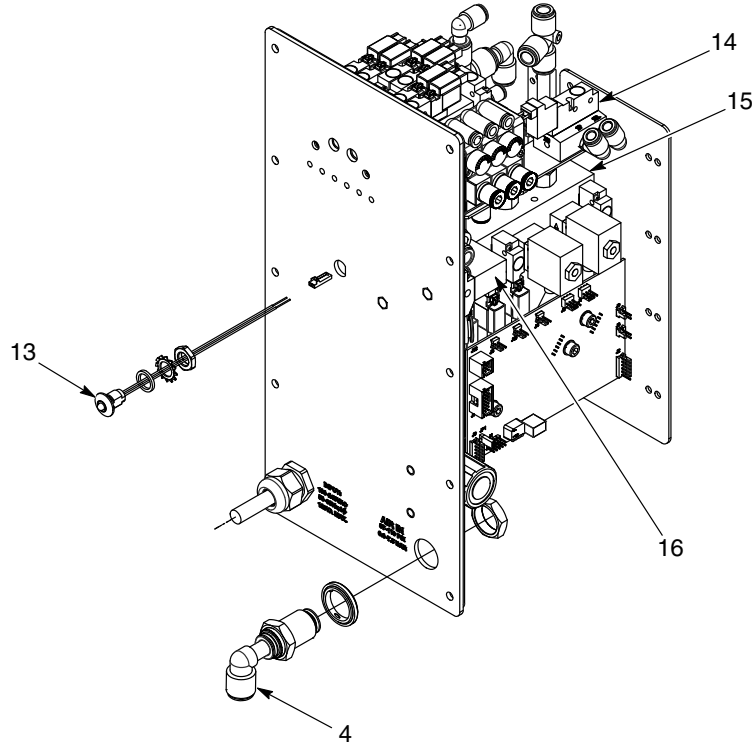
Panel Montaj Grubu Parçaları (1 / 3)
